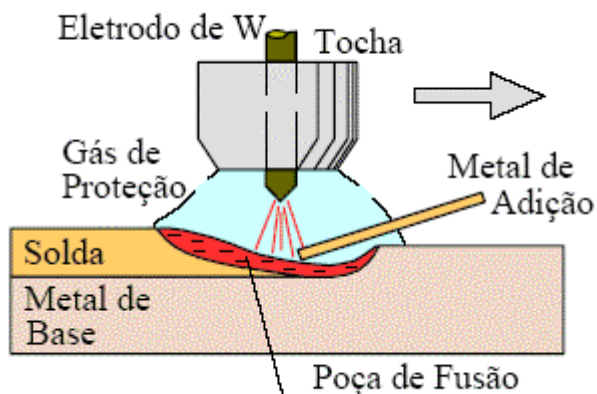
Desenho esquemático do processo de soldagem GTAW (Marques 2014)
